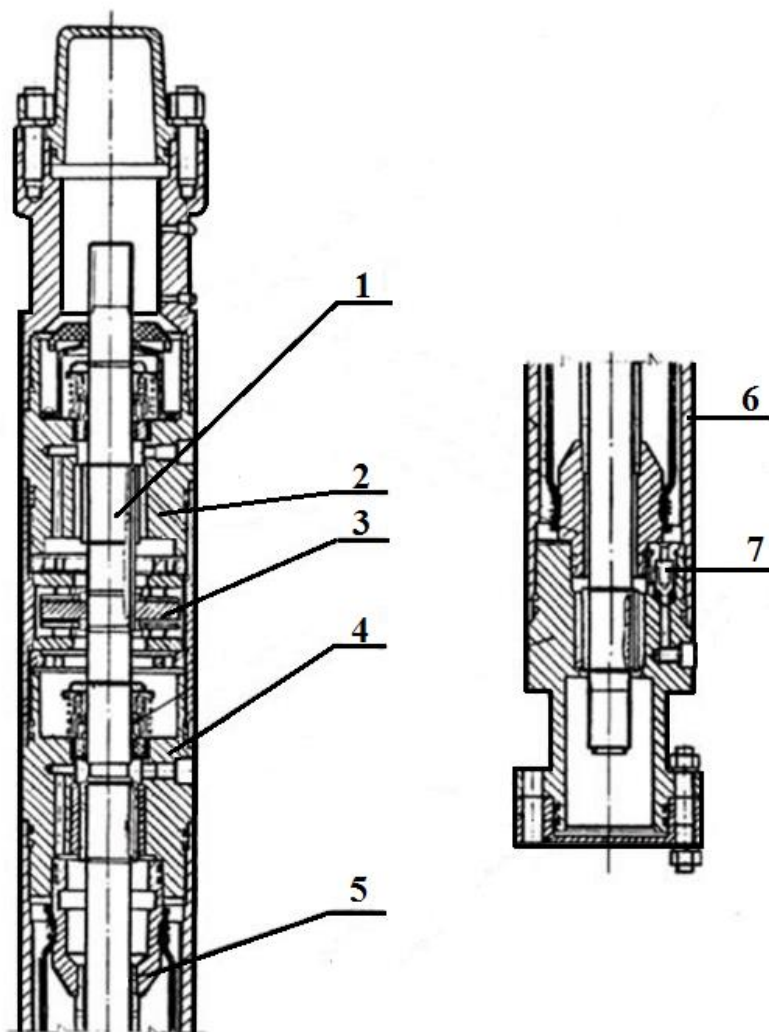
Конструкция протектора гидрозащиты типа Г:1 – вал; 2, 4 – торцовые уплотнения; 3 – упорный узел (опорная пята); 5 – мешок (диафрагма); 6 – корпус; 7 – обратный клапан.
